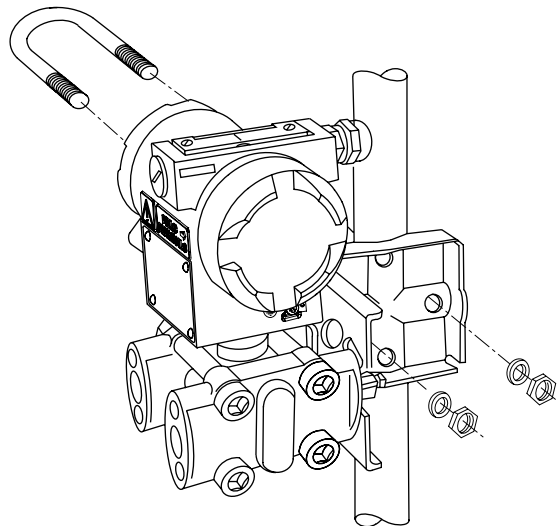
Befestigung des Messumformers mit Montagewinkel am Beispiel Differenzdruck bei waagrechten Wirkdruckleitungen
